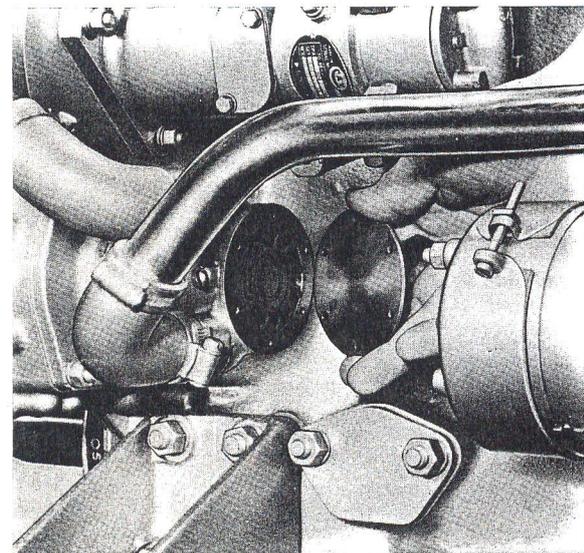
Dépose du couvercle de la pompe à eau de mer.
